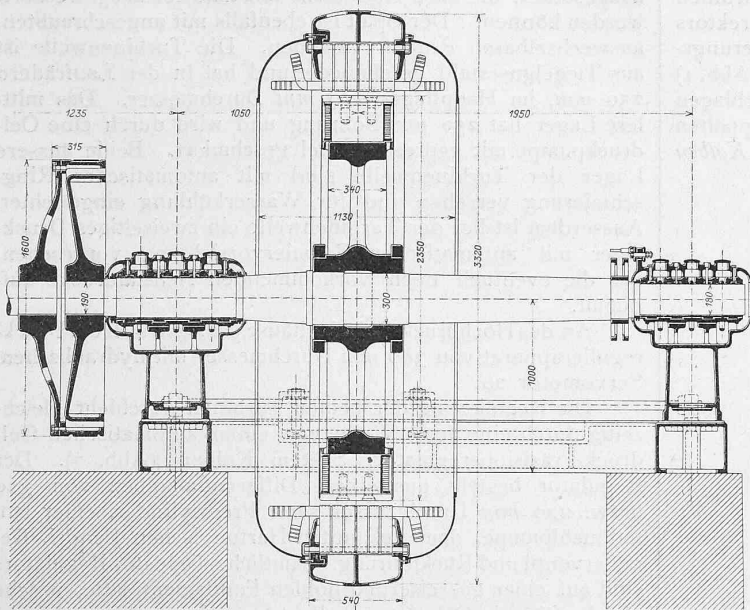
Drehstromgenerator für 1600 K. V. A., gebaut von Kolben & Cie.
